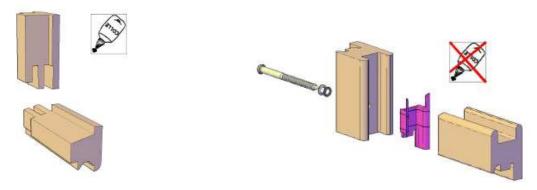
exemples d'assemblage traditionnel collé (à enfourchement) et mécanique
